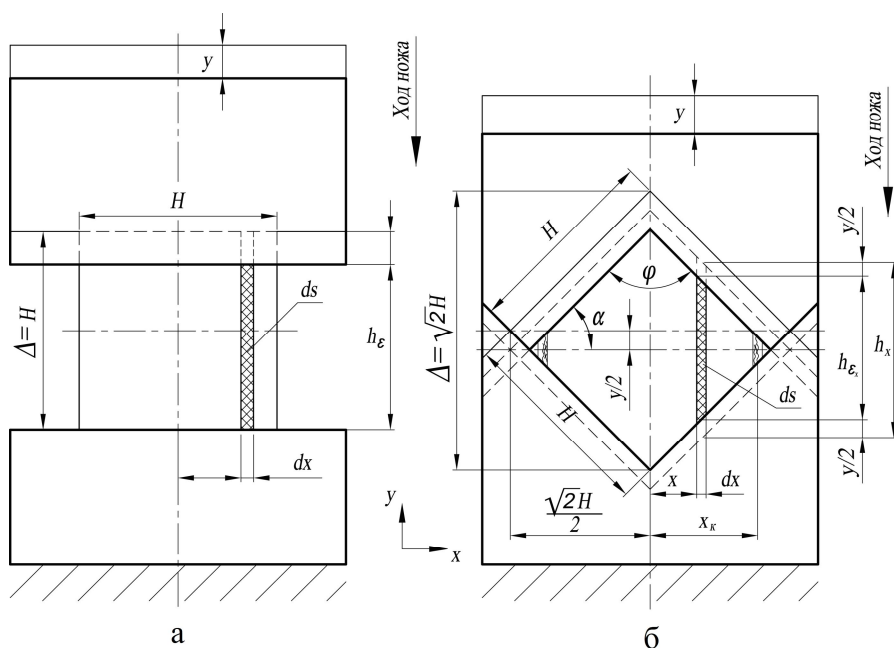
К определению силы резки квадратной заготовки параллельными (а) и фасонными (б) ножами
